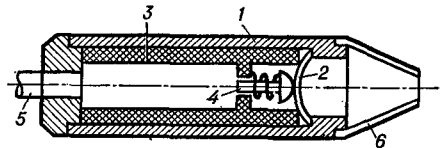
Сферический концентратор для оперативного лечения болезни Меньера: 1 — корпус; 2 — пьезокерамический фокусирующий излучатель; 3 — пластмассовая втулка; 4 — пружинный контакт; 5 — коаксиальный кабель; 6 — насадка, образующая камеру с контактной жидкостью.
